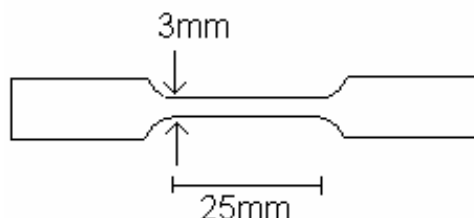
Dimensões e geometria do corpo de prova para ensaio de tração.
